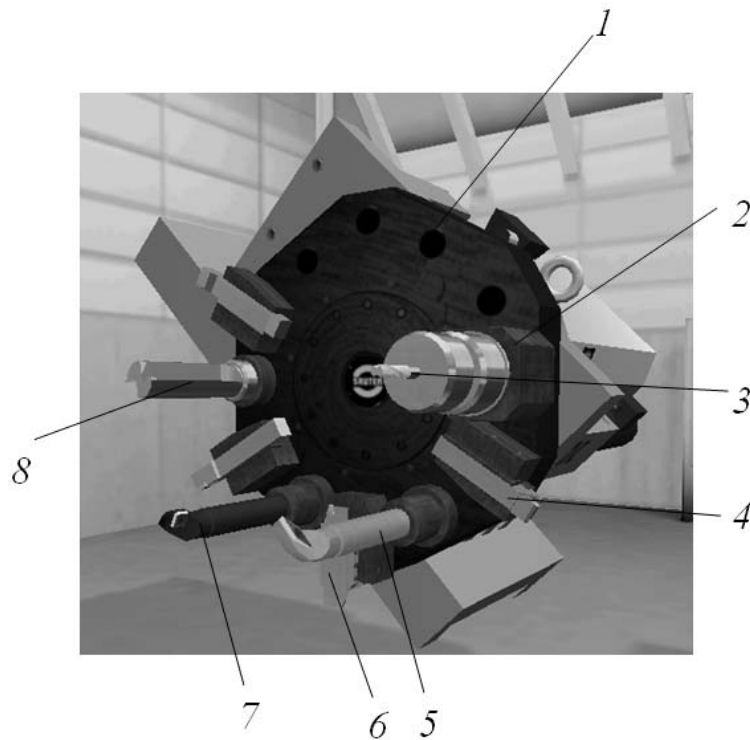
Общий вид револьверной головки токарного станка с ЧПУ
